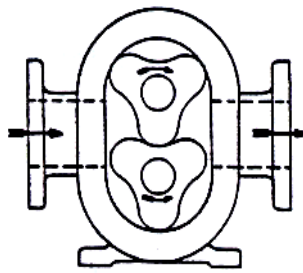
ปั๊มโรตารีแบบเกียร์ (Gear type)
